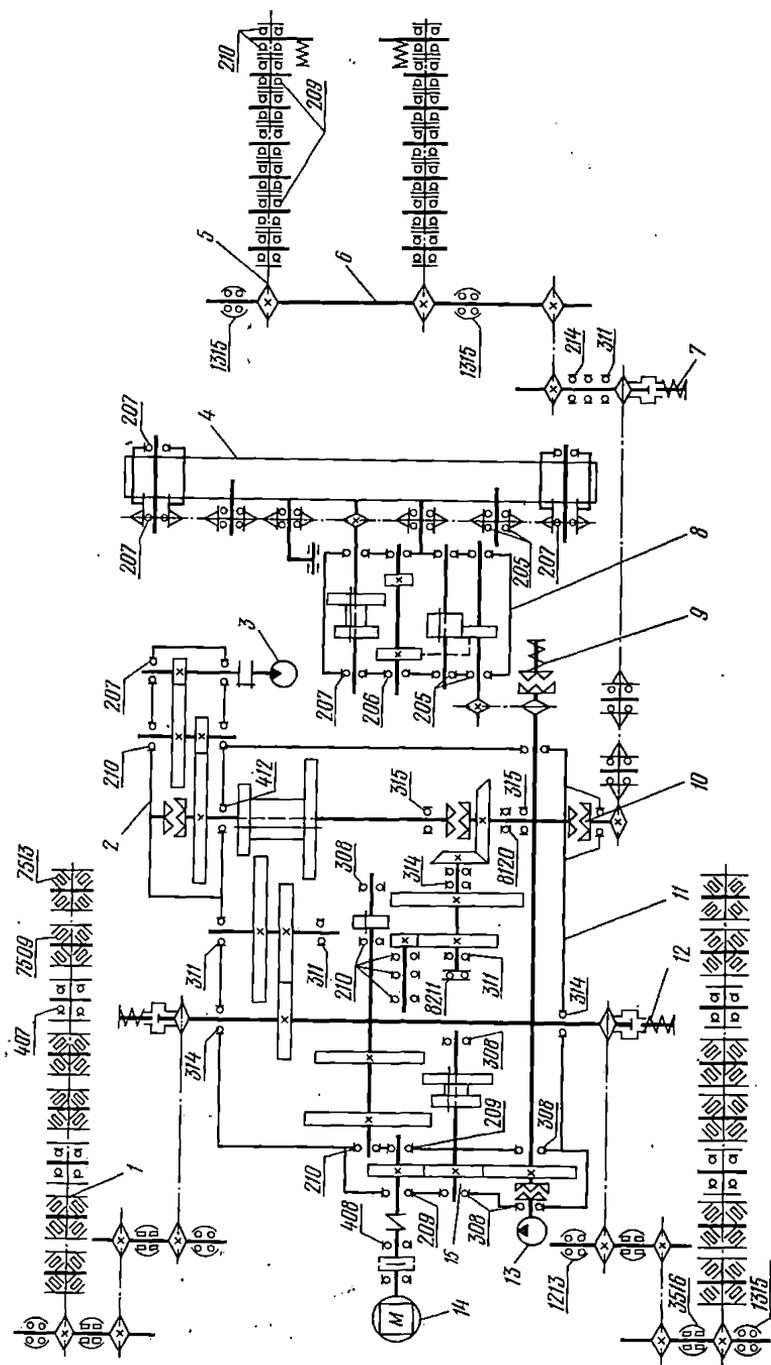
Кинематическая схема экскаватора ЭПЦ-202А:
